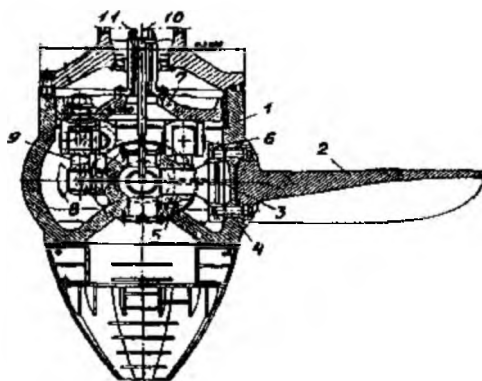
Механизм поворота лопастей рабочего колеса турбины Саратовской ГЭС
